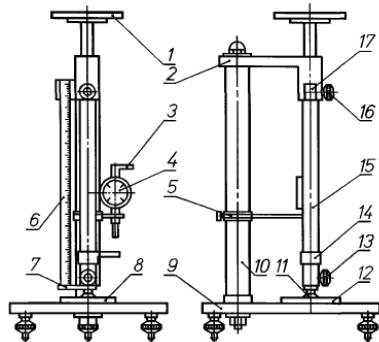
Прибор для определения сжимаемости и упругости: 1 – стол; 2 – направляющая; 3 – фиксатор; 4 – индикатор; 5 – держатель; 6 – шкала; 7 – кронштейн; 8 – пластина; 9 – основание; 10 – опора; 11 – палец; 12 – держатель; 13 – винт; 14 – опора; 15 – шток; 16 – винт; 17 – кронштейн
